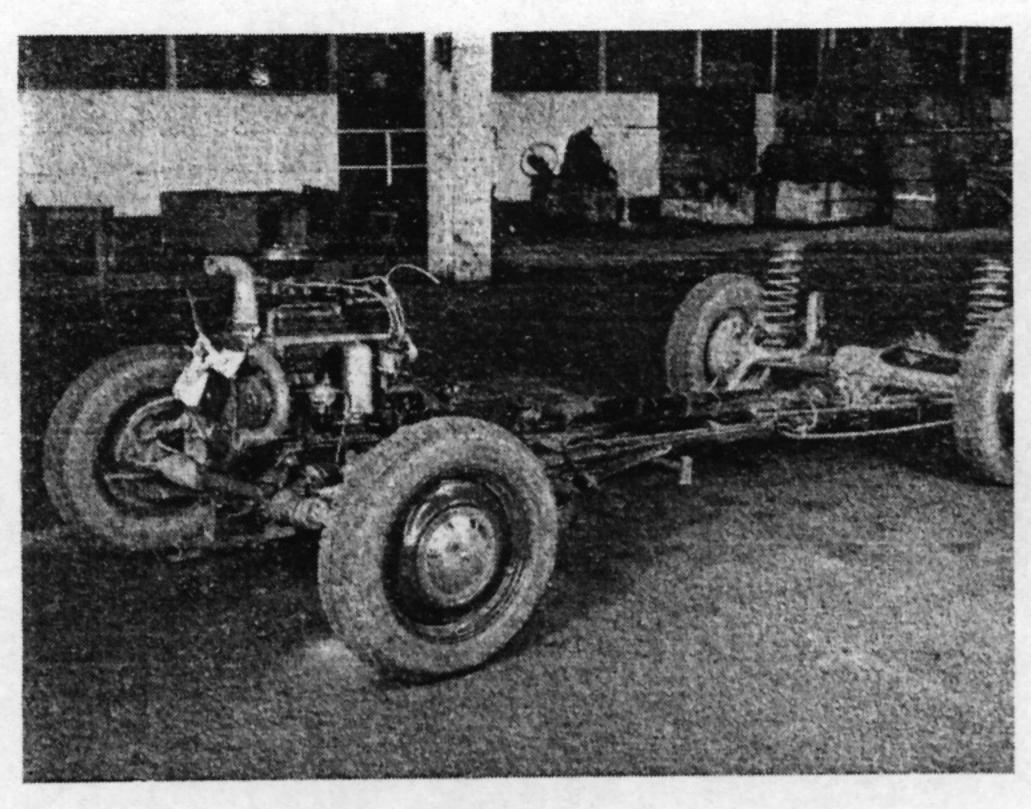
L'ensemble mécanique soutenu par le faux châssis
